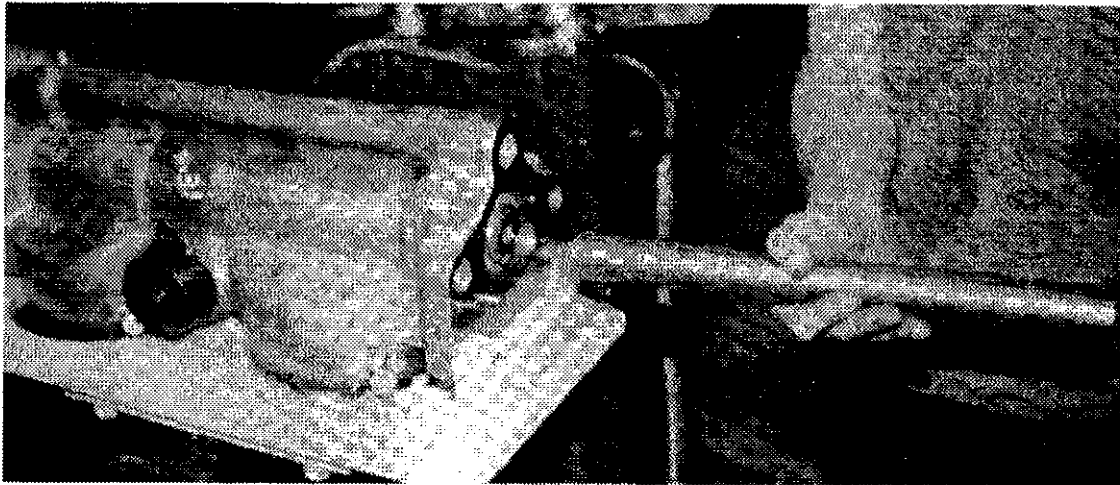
Desmontaje del rodamiento trasero y del separador
